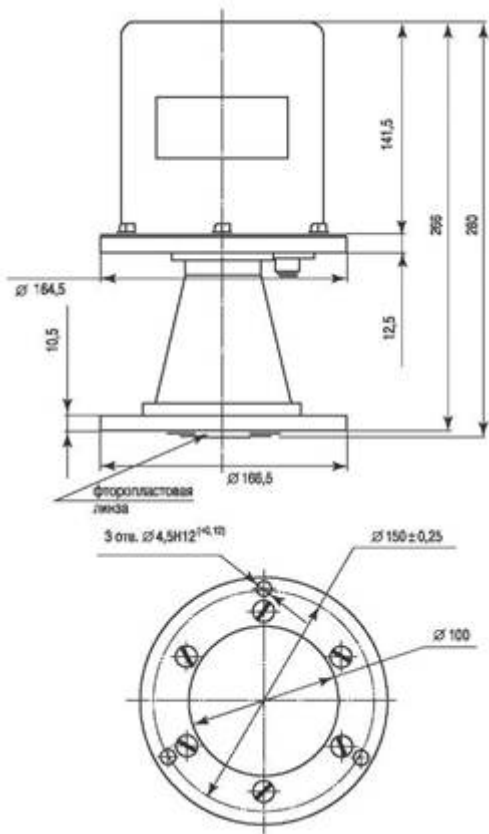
Габаритные, установочные и присоединительные размеры датчика уровня РДУ-Х8, РДУ-Х8И
